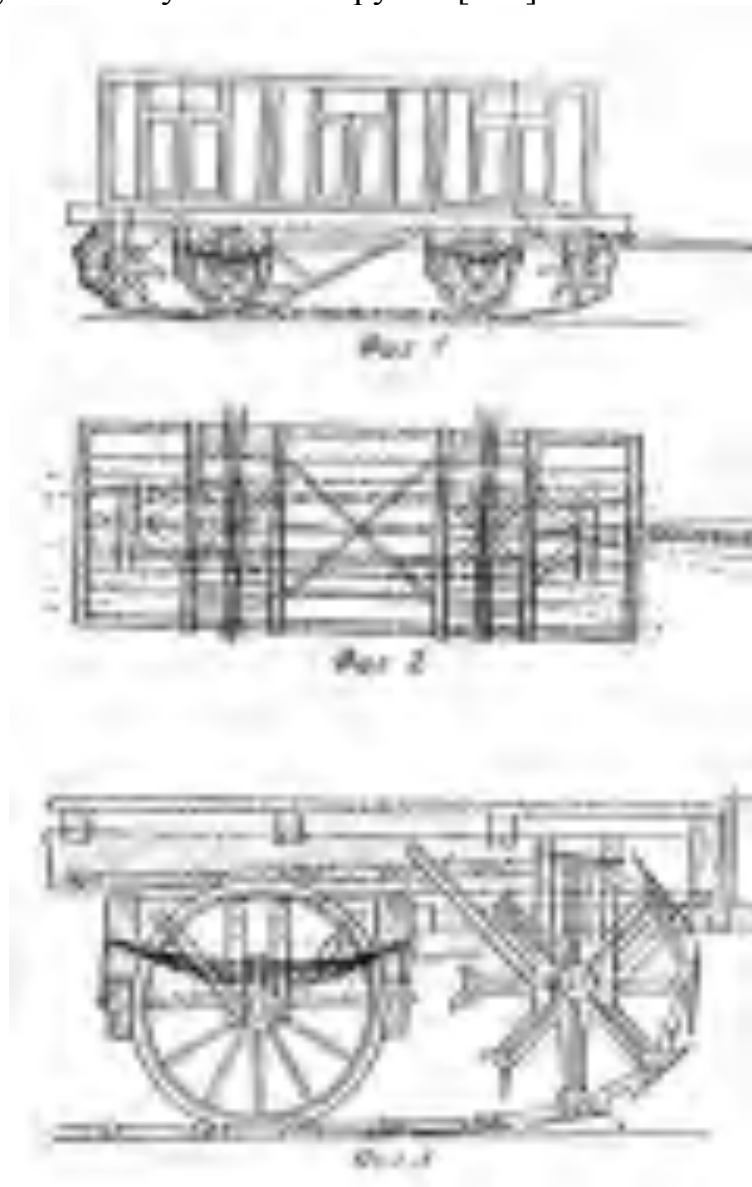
24. Креслення вагона з нескінченними рейками Ф.А. Блінова
